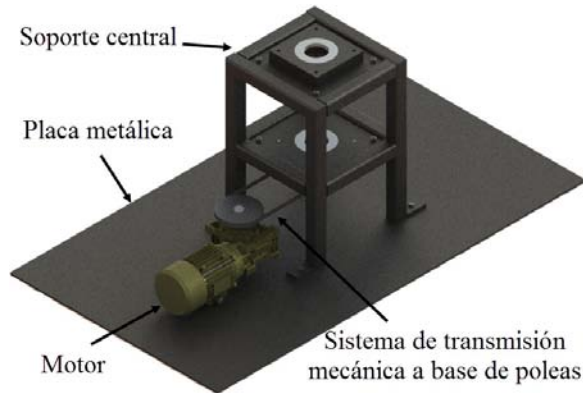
Componentes no rotatorios: a) Soporte central, b) Placa metálica, c) Motor, d) Sistema de transmisión mecánica a base de poleas.
